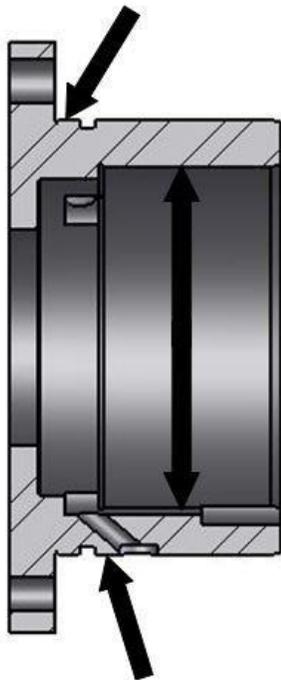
Áreas de inspección - Grupo 3 de la caja de rodamientos
